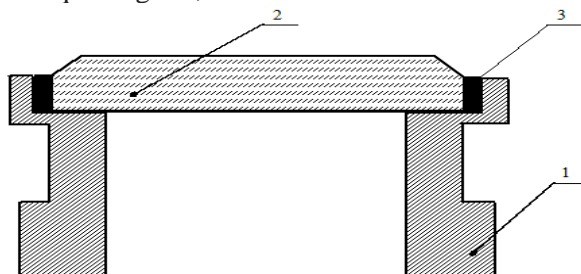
Схема охоплюючого з'єднання паянням кварцового скла з алюмінієм: 1 — алюмінієвий фланець; 2 — кварцове скло; 3 — припій
